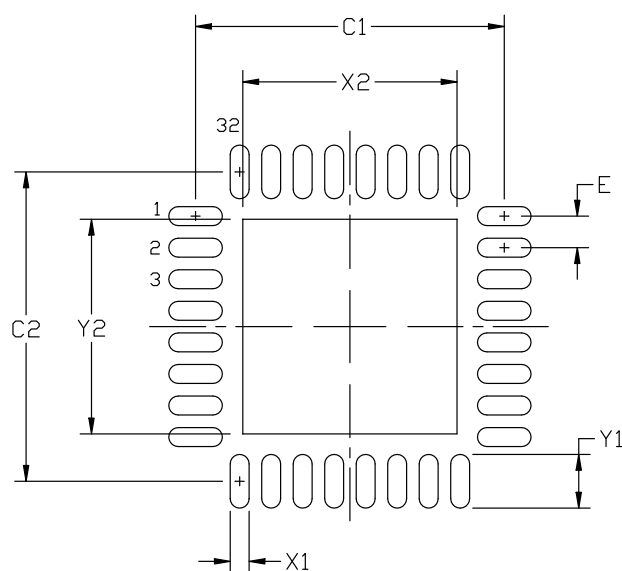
QFN32 PCB 焊盘布局图
